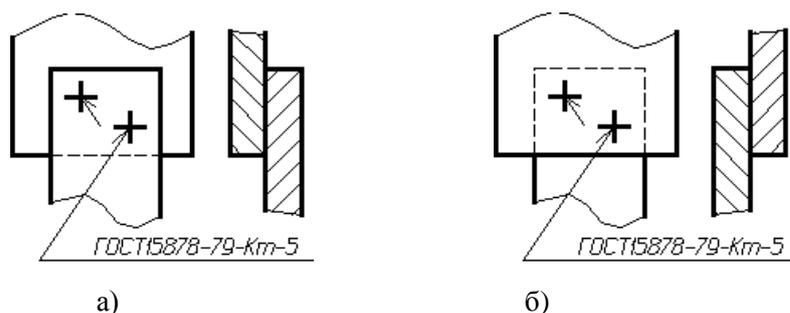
Одиночные сварные точки соединения внахлестку, выполняемые контактной точечной сваркой: а) с лицевой стороны; б) с оборотной стороны
